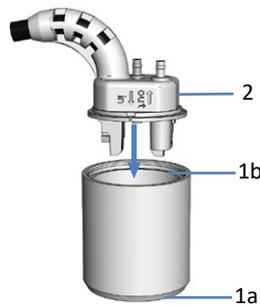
Montage des pièces du détecteur de rinçage des joints
